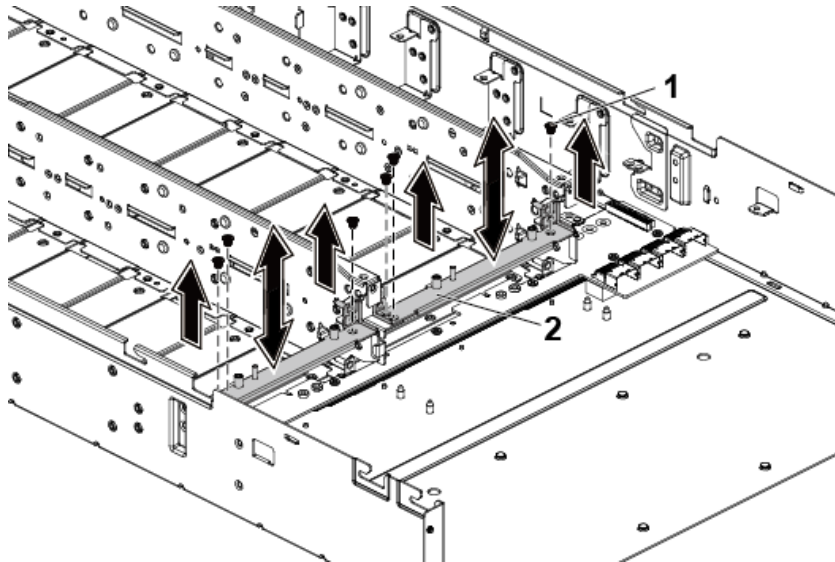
Entfernen und Einbauen der Mittelplattenhalterung
